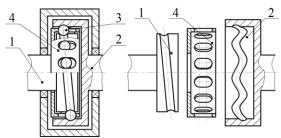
Фрикционно-зубчатая передача с промежуточными телами качения: 1) фрикционное колесо; 2) зубчатое колесо; 3) промежуточное тело качения; 4) сепаратор
